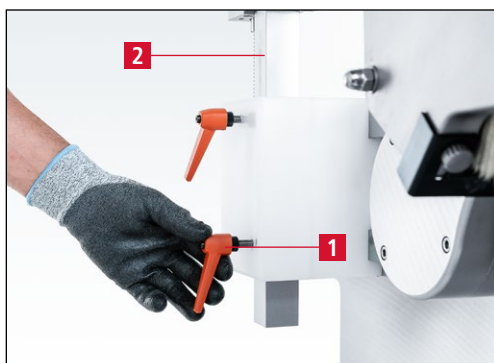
Регулировка ножа в центре шлифовального круга
